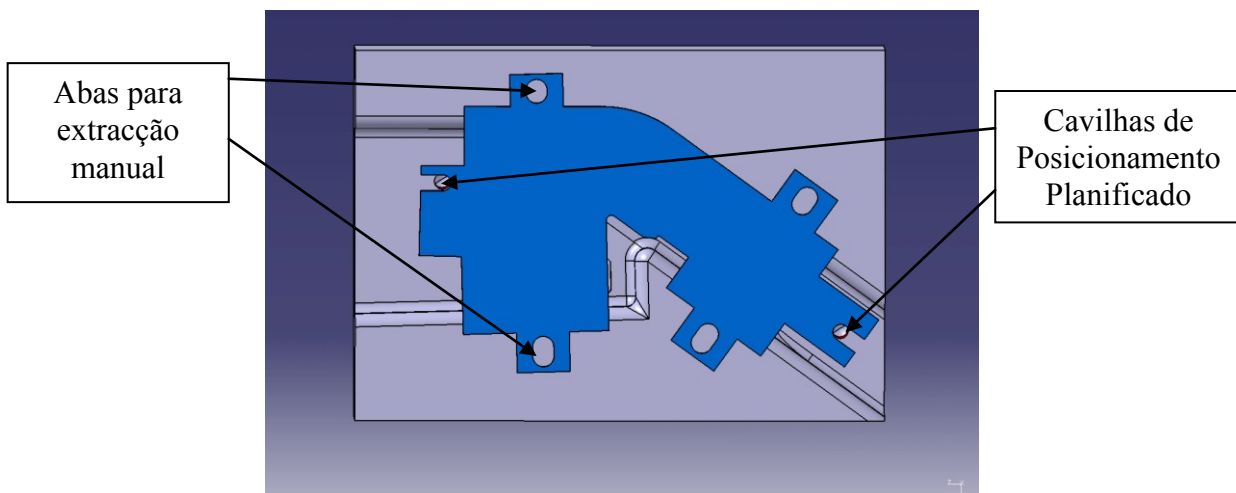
Definição do planificado após modelação de ferramenta de estampagem
